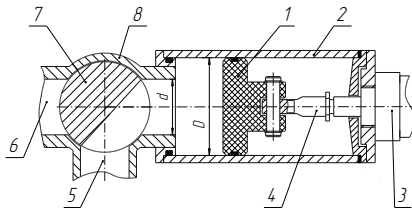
Принципова схема поршневого дозатора: D – діаметр мірного циліндра, d – діаметр випускного каналу; 1 – поршень; 2 – мірний циліндр; 3 – приводний механізм; 4 – шток; 5 – випускний канал; 6 – впускний канал; 7 – кранова запірна система; 8 – корпус.
